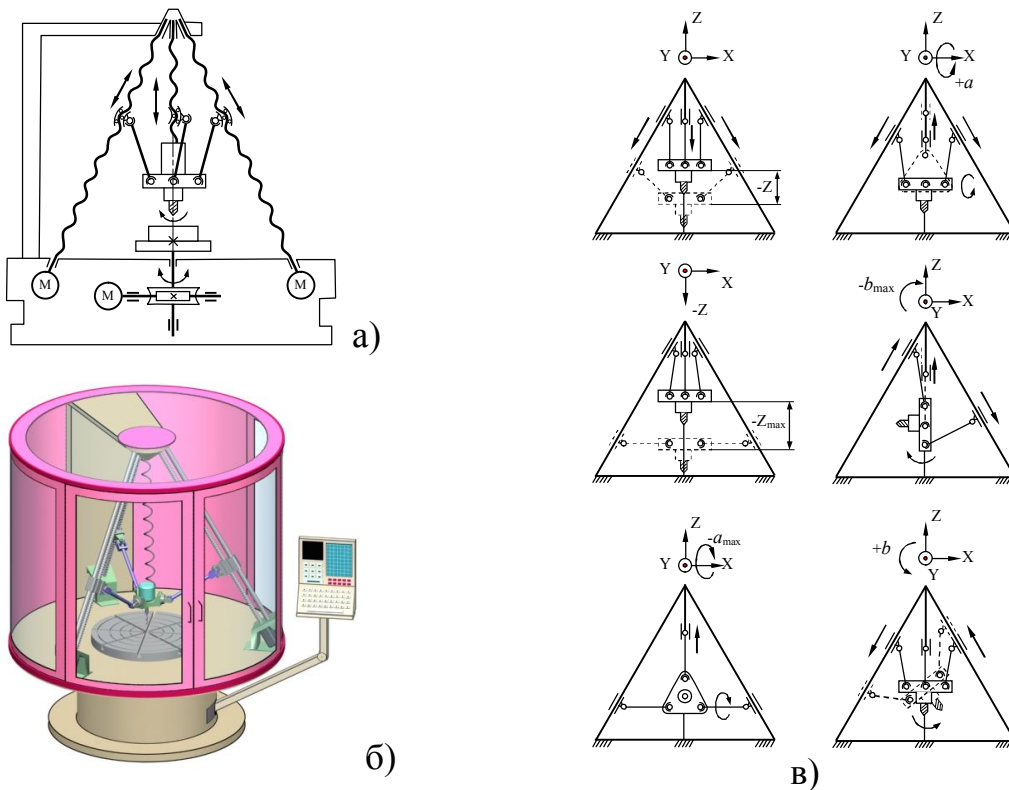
Багатокоординатний свердильно-фрезерний верстат пірамідальної компоновки: а – кінематична схема; б – загальний вид; в – основні технологічні рухи по керованим координатам
